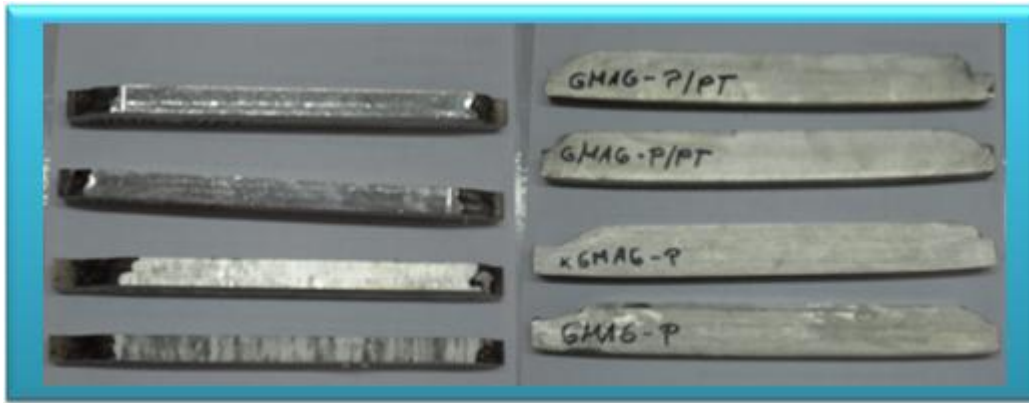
Probetas de los revestimientos soldados para doblez longitudinal
